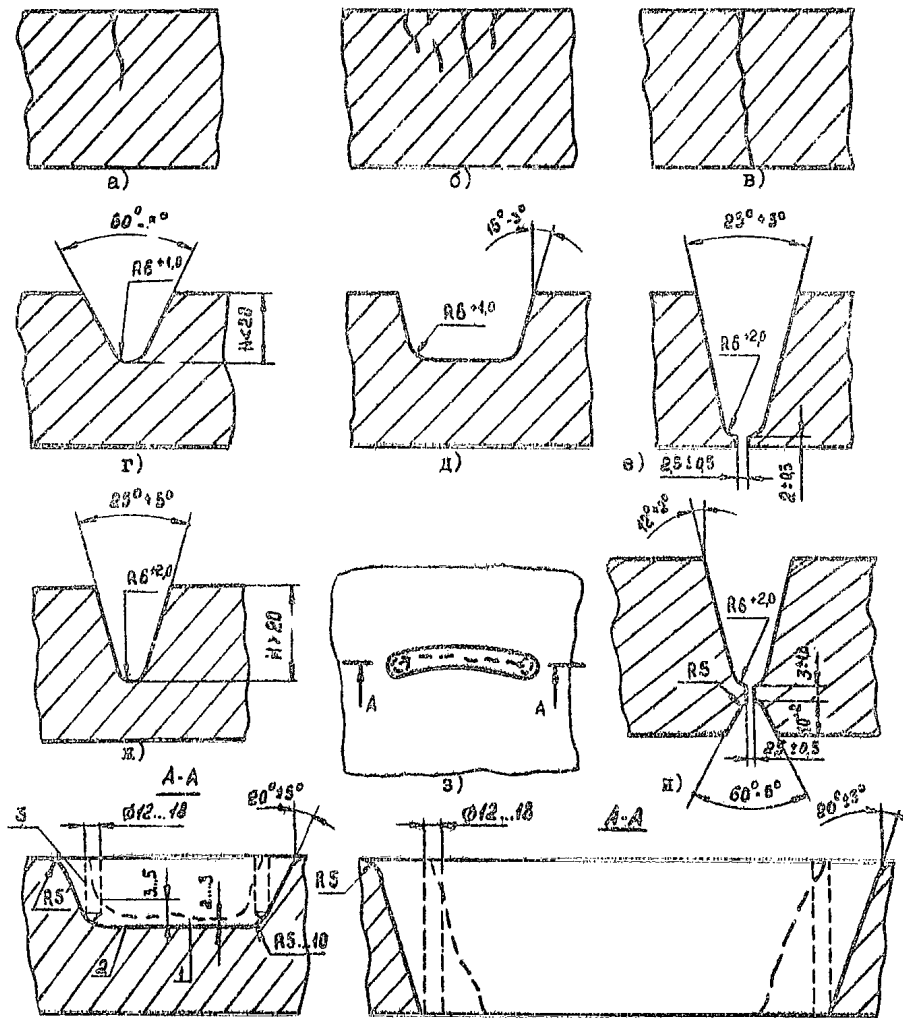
Разделка сквозных и несквозных трещин под дуговую сварку.
